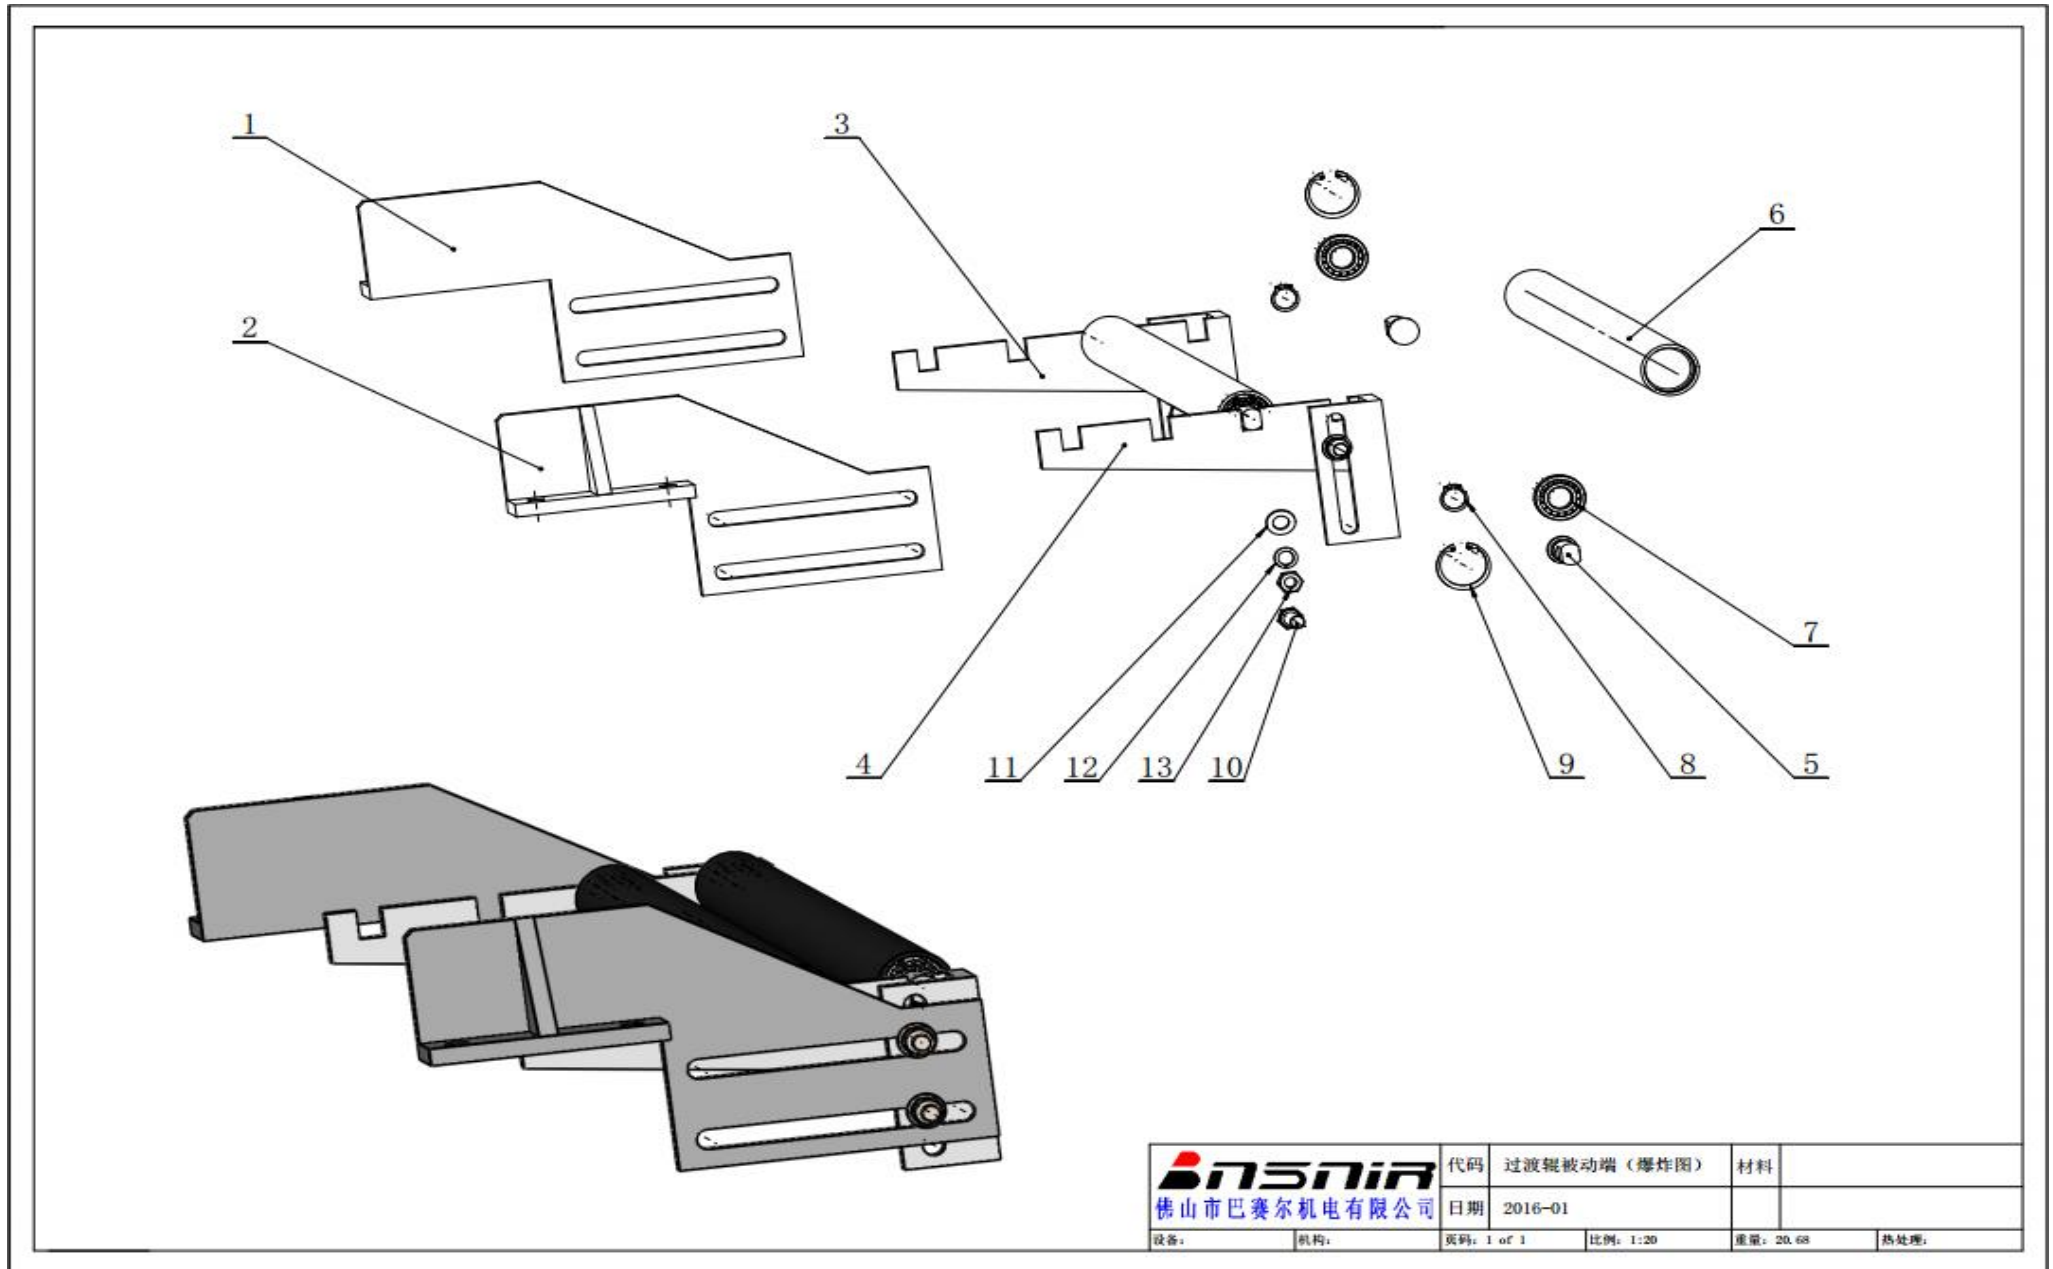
3 机架部分——过渡辊被动端装配图 picture2-3 Gantry part -- Assembly diagram of passive end of transition roll
